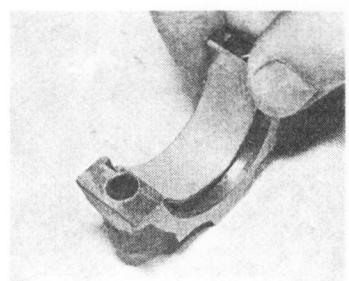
Установите вкладыши в шатун и в крышку подшипника...
